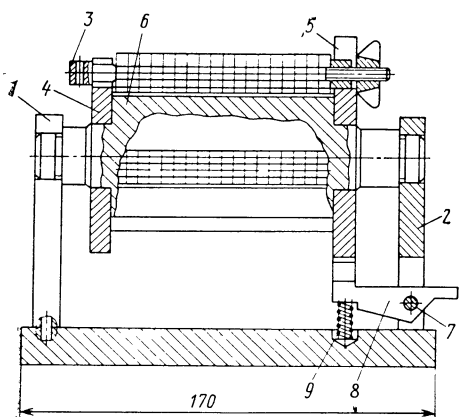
Многоместное приспособление для заточки задних поверхностей твердосплавных пластин и ножей
